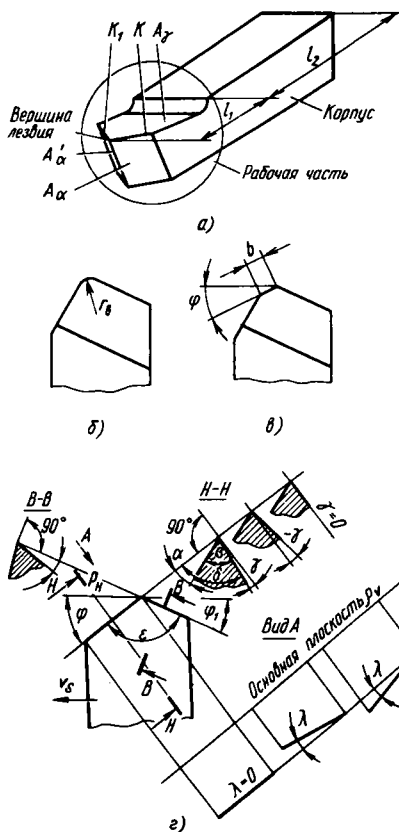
Конструктивные элементы и геометрические параметры резцов
